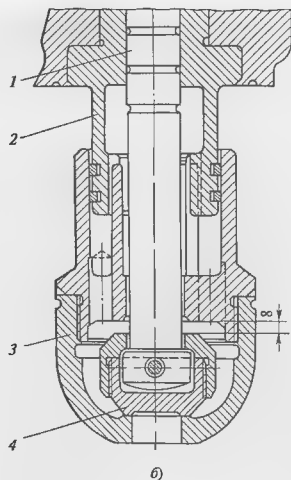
Разгруженный регулирующий клапан ЛМЗ
